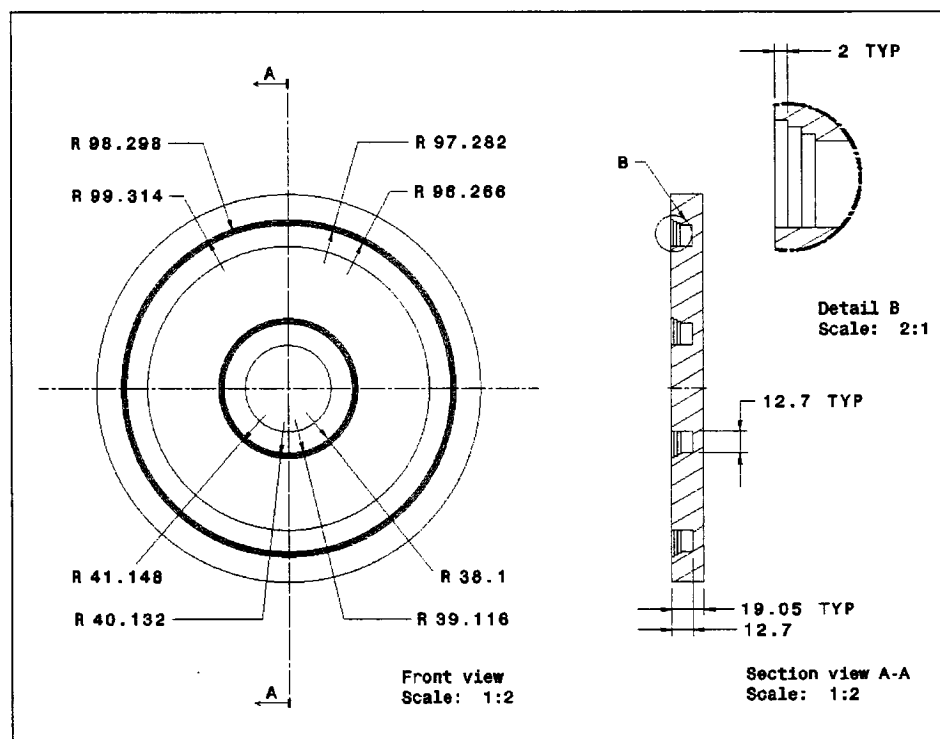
Pièce utilisée pour les tests d'usinage (les dimensions sont en mm)
